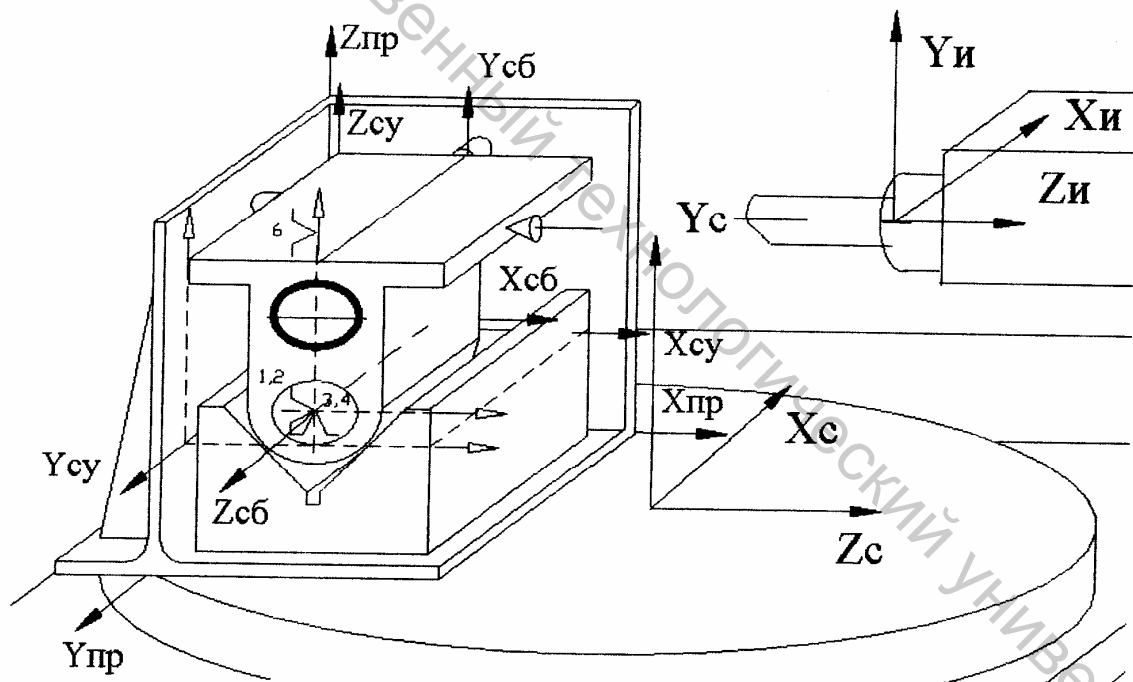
Пример взаимного расположения систем координат: сб- заготовки (собственной или базовой системы координат; су- схемы установки; пр- приспособления; с- станка; и- инструмента.
